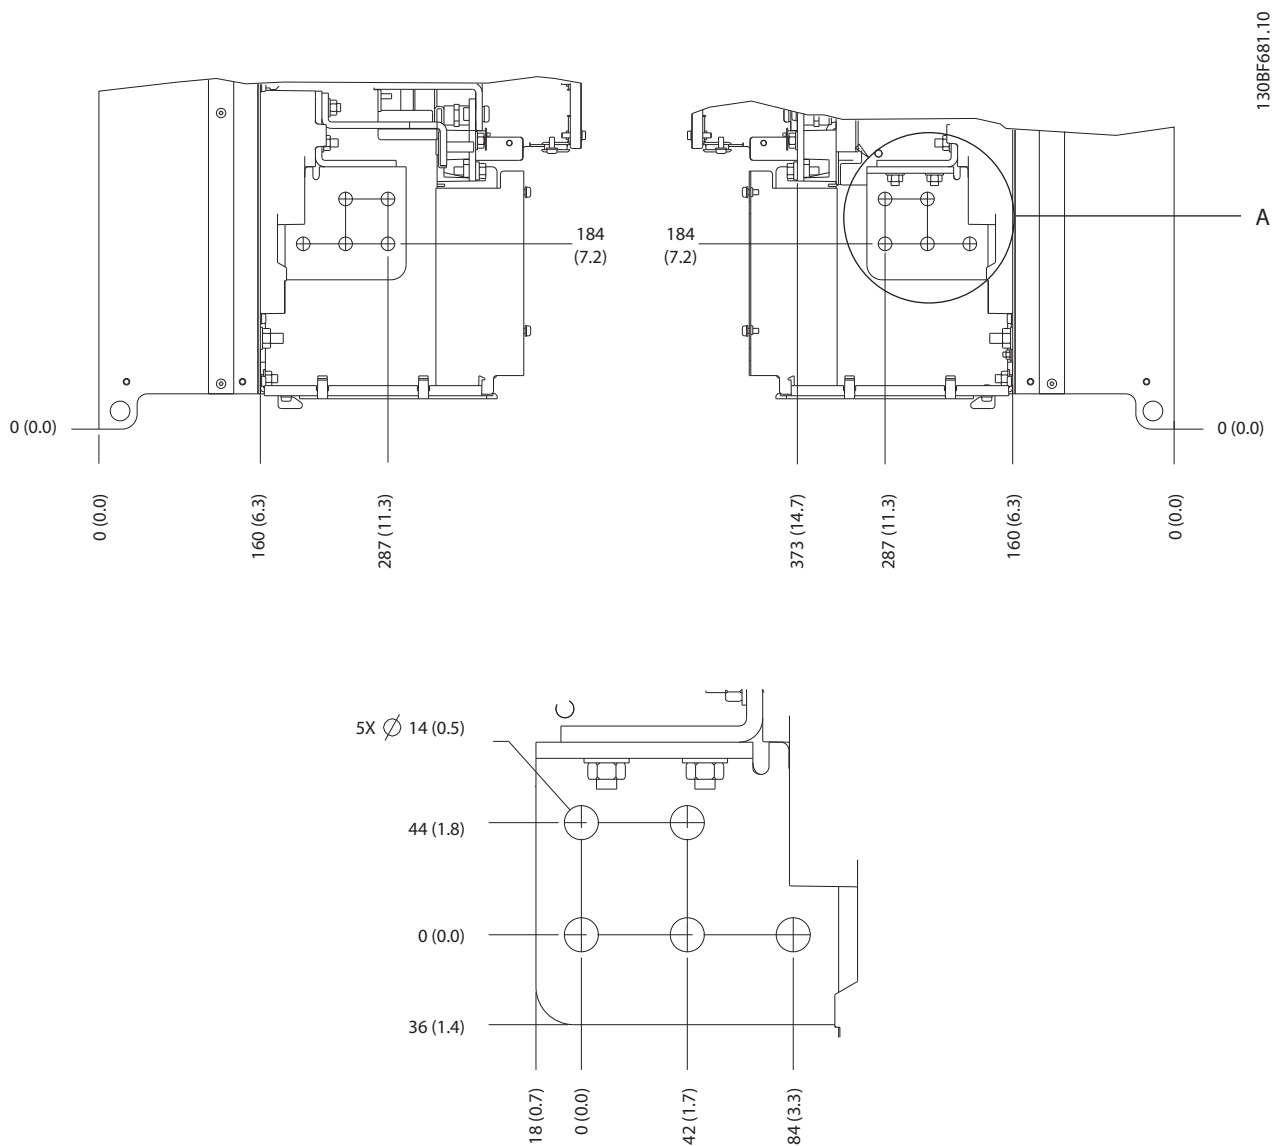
Terminação de blindagem de RFI e dimensões da chapa para entrada de cabos do E4h
